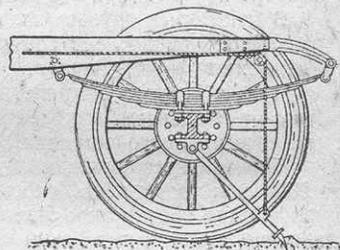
Горный упор, прикрепленный к задней оси грузового автомобиля с цепной передачей.
